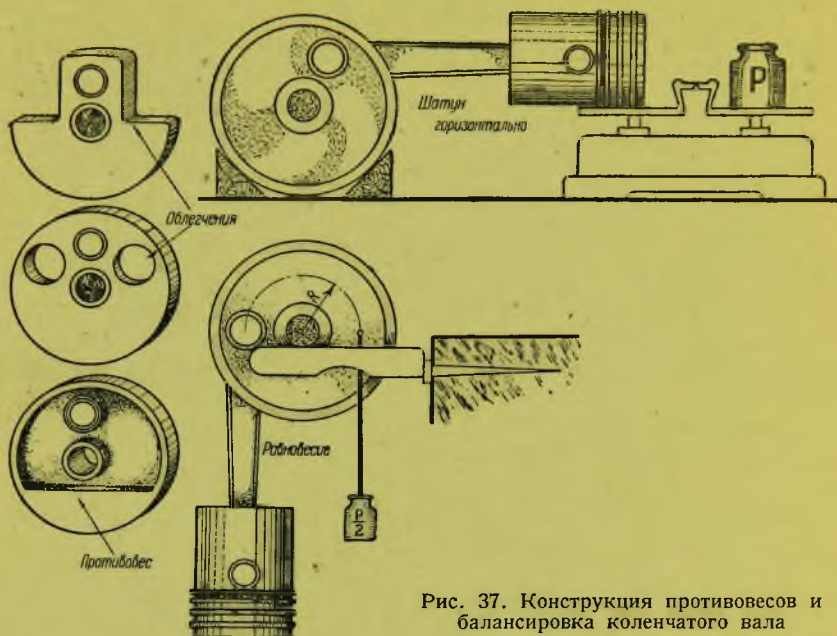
Конструкция противовесов и балансировка коленчатого вала
